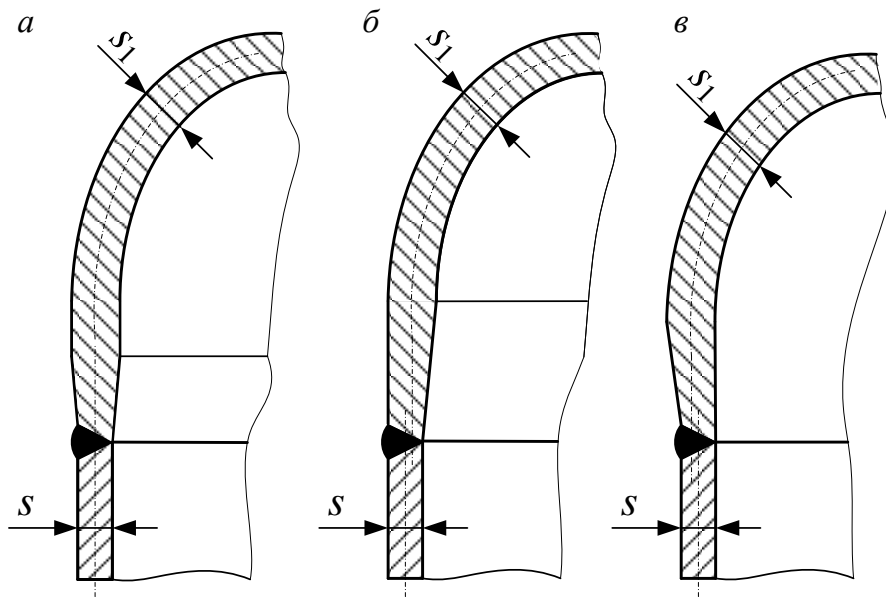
Варіанти обробки днищ перед зваркою:
